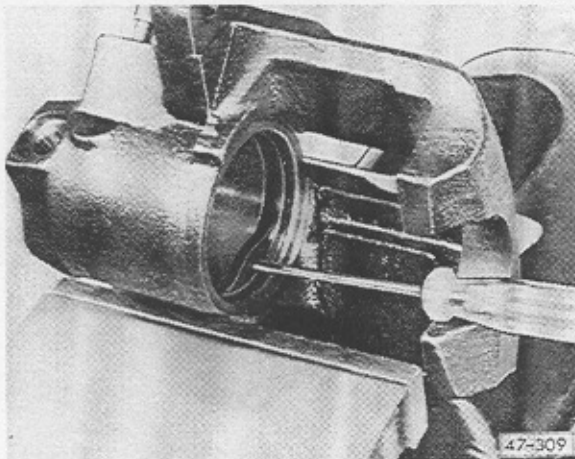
Dichtring vorsichtig mit einem Schraubenzieher herausnehmen
